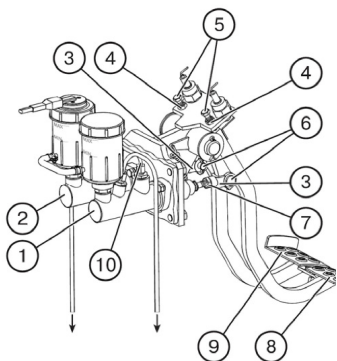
Регулировка хода педалей тормозов: 1, 2 – гидроцилиндры; 3 – вилки; 4, 7 – контргайки; 5 – регулировочный болт; 6 – палец; 8, 9 – педали тормозов; 10 – трубка
